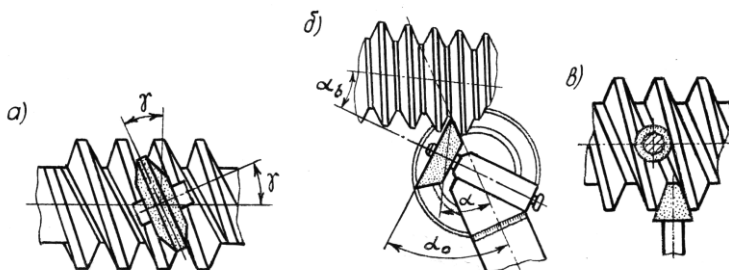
Схемы установки шлифовальных кругов при шлифовании архимедовых червяков ZA: а – схема установки дискового круга
